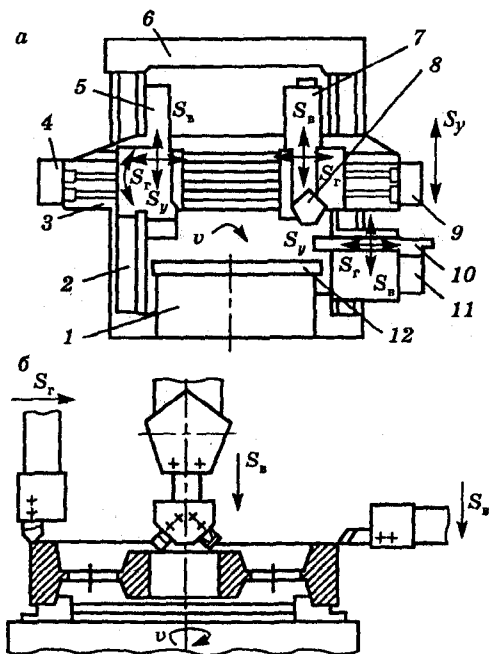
Токарно-карусельный станок (а) и схема обработки на нем заготовки (б)
